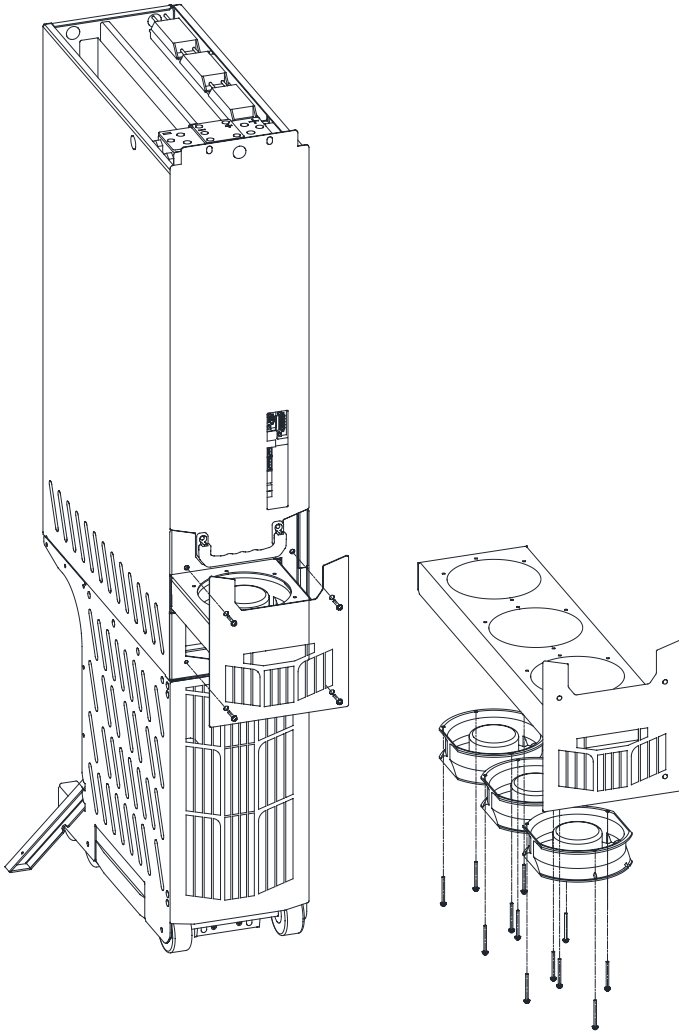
Замена вентилятора инверторного блока типоразмера Н8
